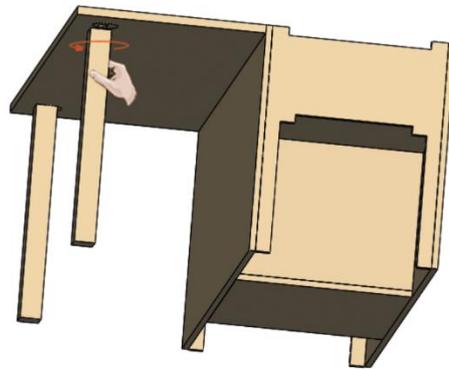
Paso 21 del ensamblaje del baúl (conjunto 1)
